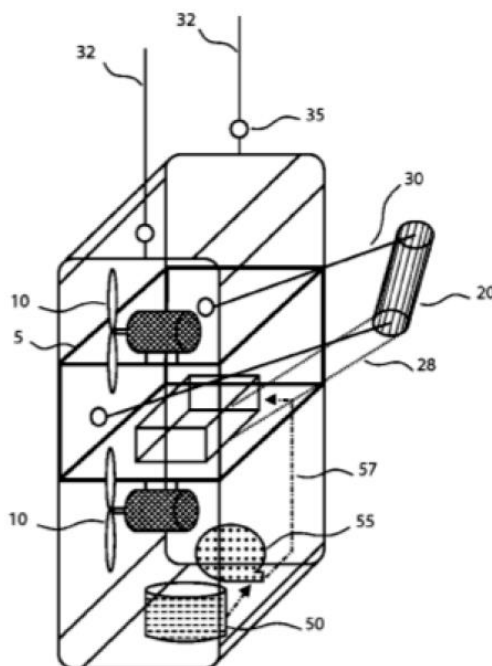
Aparato de limpieza de fachadas en vidrio. [39]
